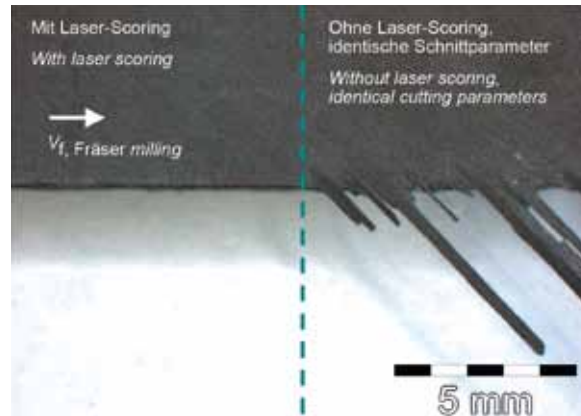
CFK-Bauteilkante, bearbeitet mit verschlissenenem Werkzeug durch Laser-Scored-Machining (LSM) und konventionelles Besäumfräsen
